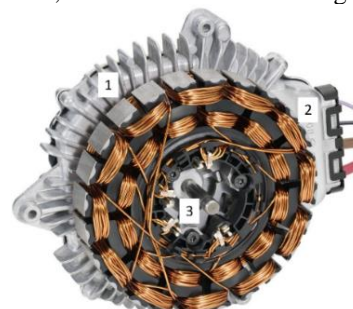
Bobinado de un motor ECM, (Robert Bosch GmbH, 2019).
